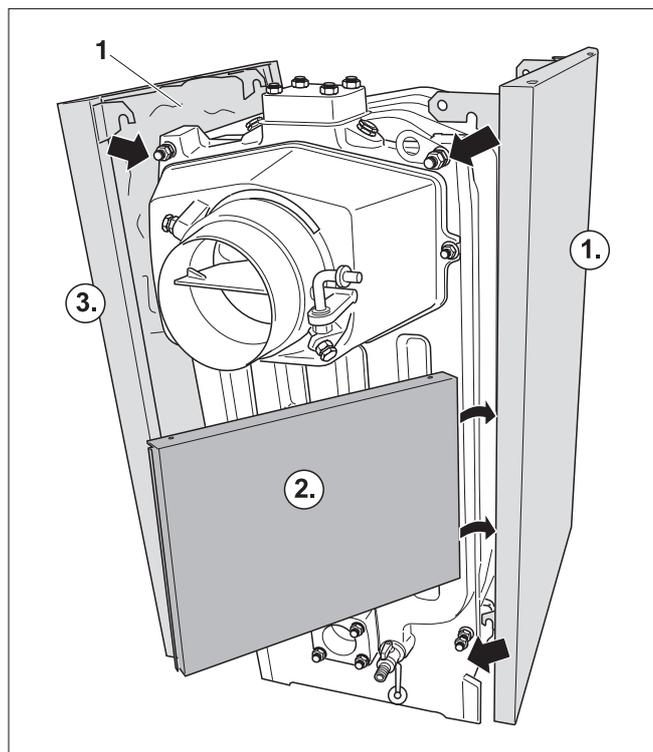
Montage des panneaux latéraux et du panneau arrière
